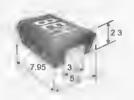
Внешний вид и размеры корпуса DO-214AB
